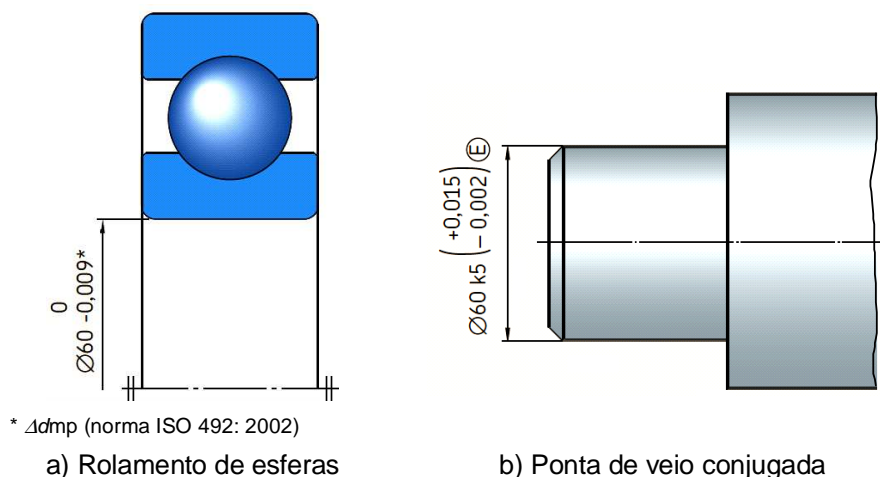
Exemplo de toleranciamento dimensional do anel interno de um rolamento de esferas e da sua ponta de veio conjugada. Adaptada de [W3]
